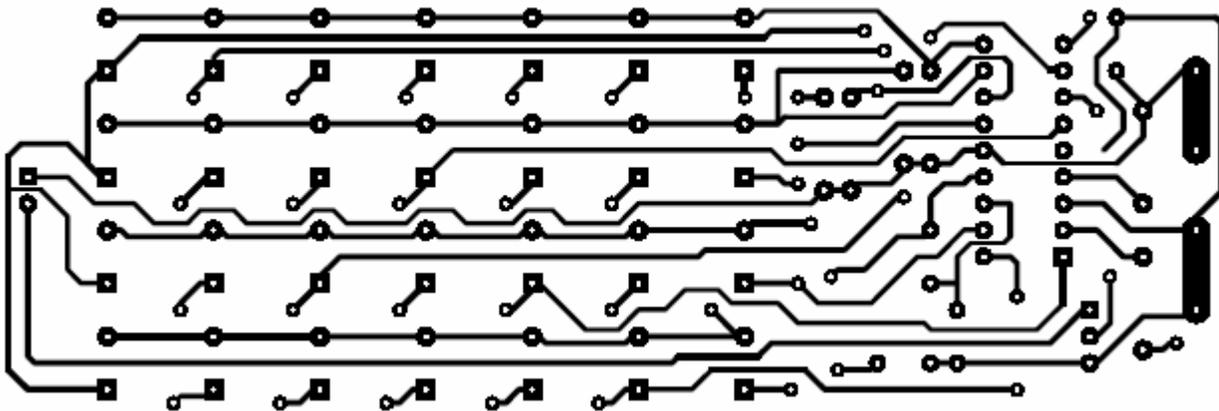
Circuito impreso del control remoto (lado de la soldadura).
